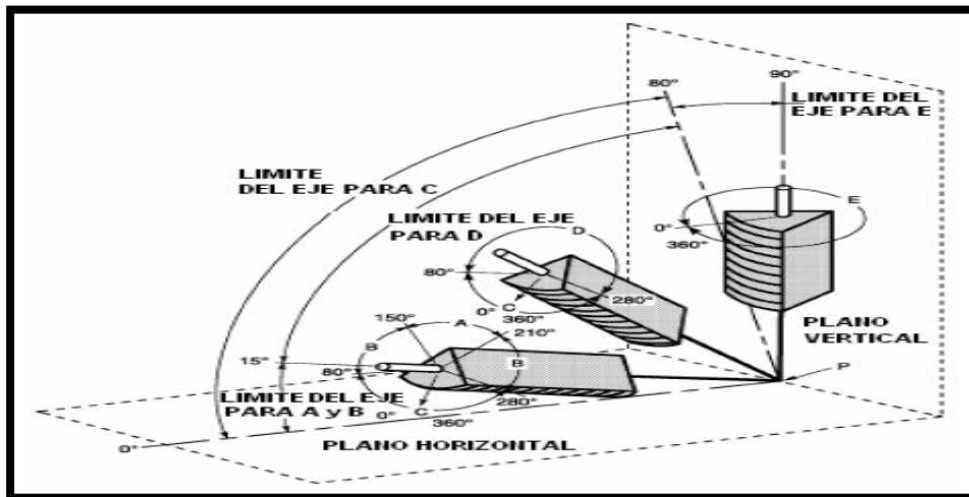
Posicionamiento de las soldaduras de ranura
